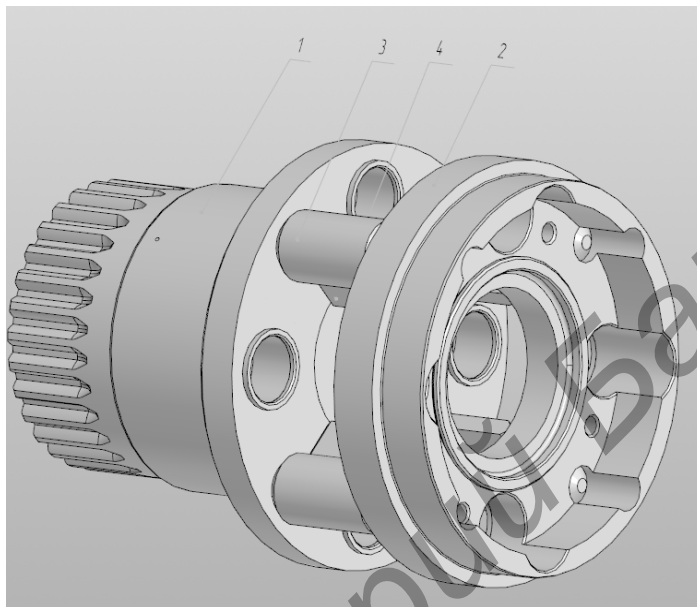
Водило, изготовленное методом сварки
